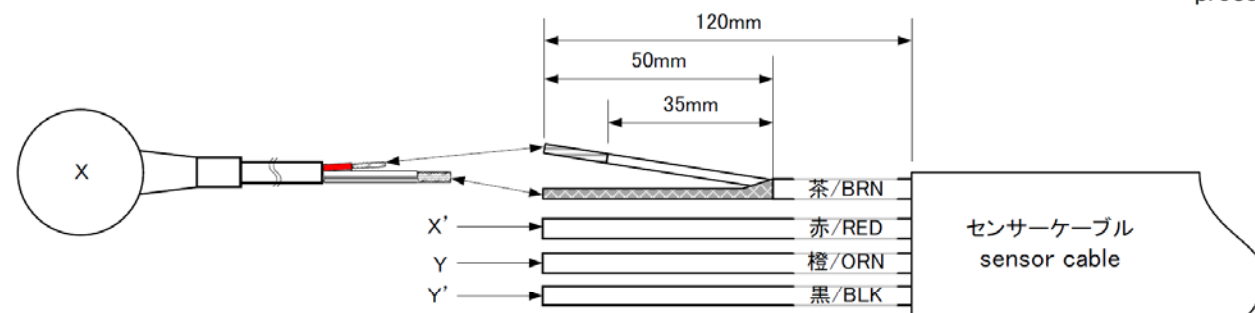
センサーケーブル端末加工図と接続/FIG. 3. Sensor cable terminal processing drawing and connection
